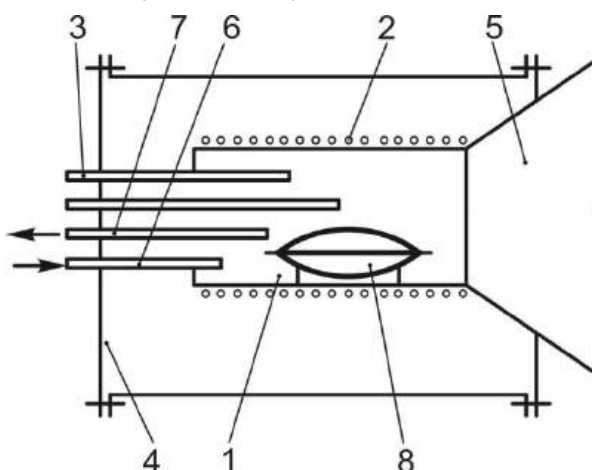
Принципова схема компресійної печі: 1 – камера; 2 – нагрівач; 3 – термopари; 4 – корпус; 5 – кришка; 6 – канал для подавання аргону; 7 – канал системи вакуумування; 8 – заготовка з матрицею
